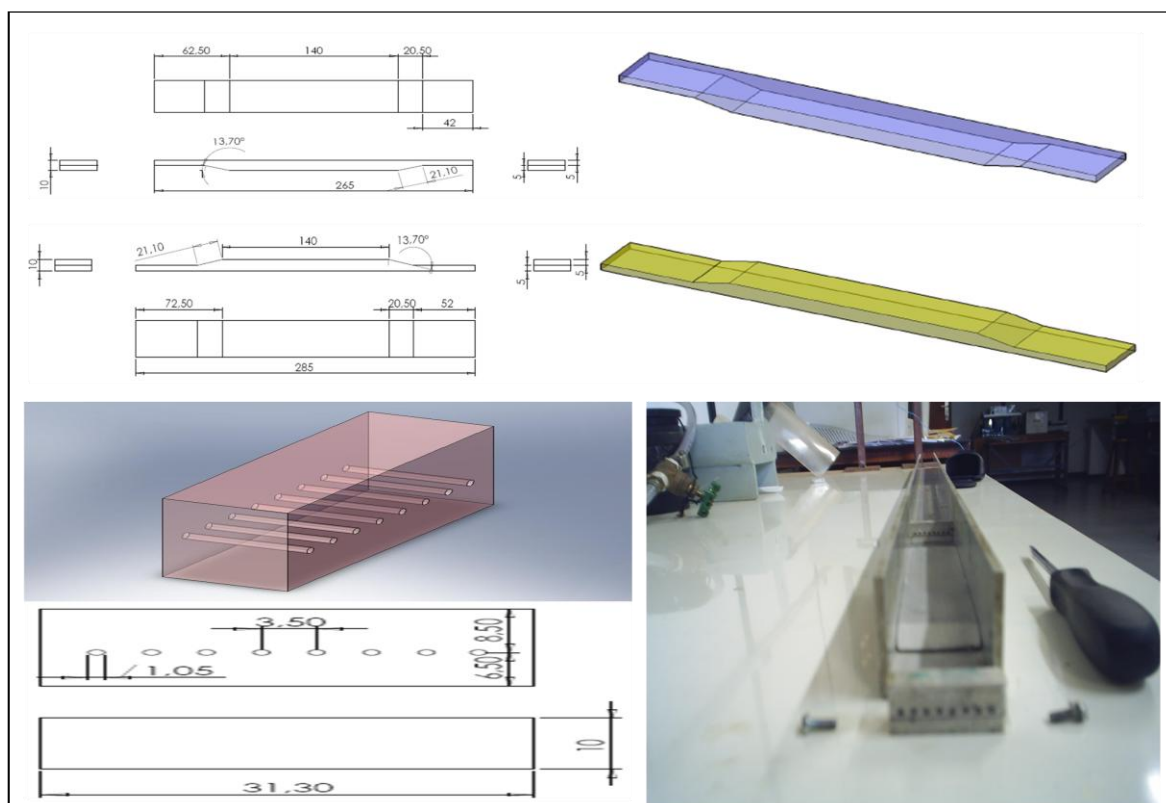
Detalhamento esquemático do molde, dimensões em mm.
